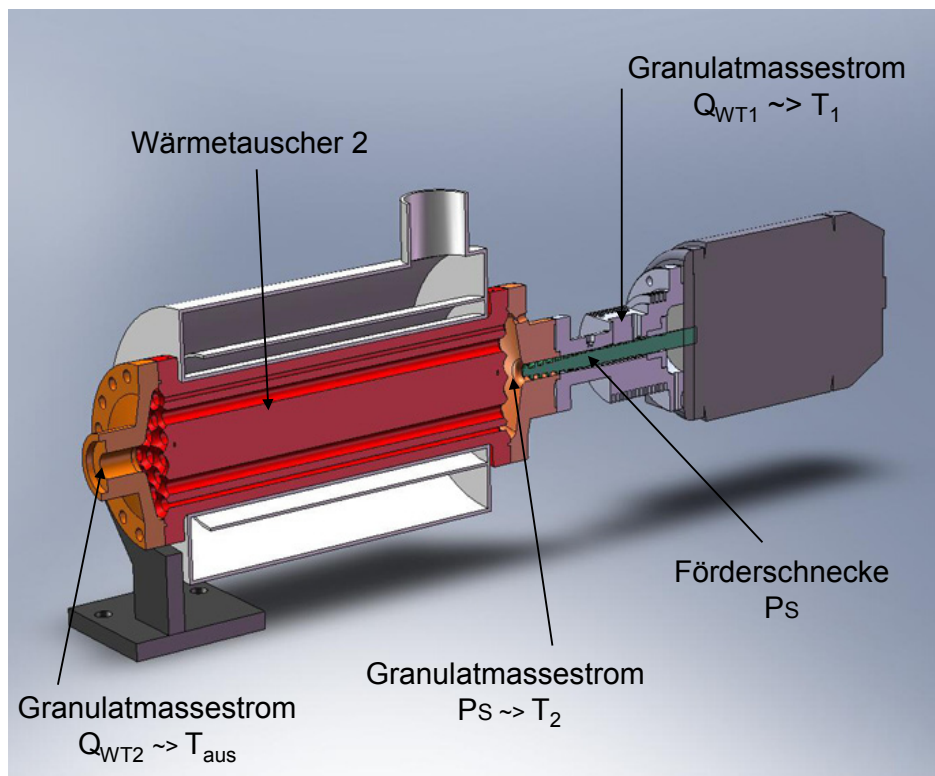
Baugruppenkonstruktion Schnittdarstellung
